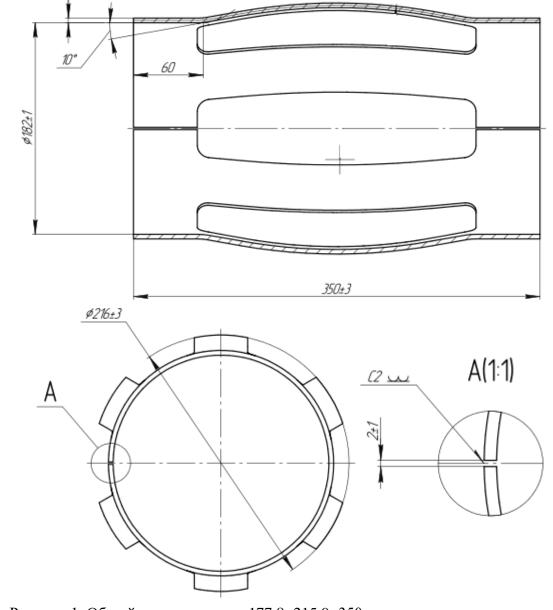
Общий вид центратора 177,8×215,9×350.
